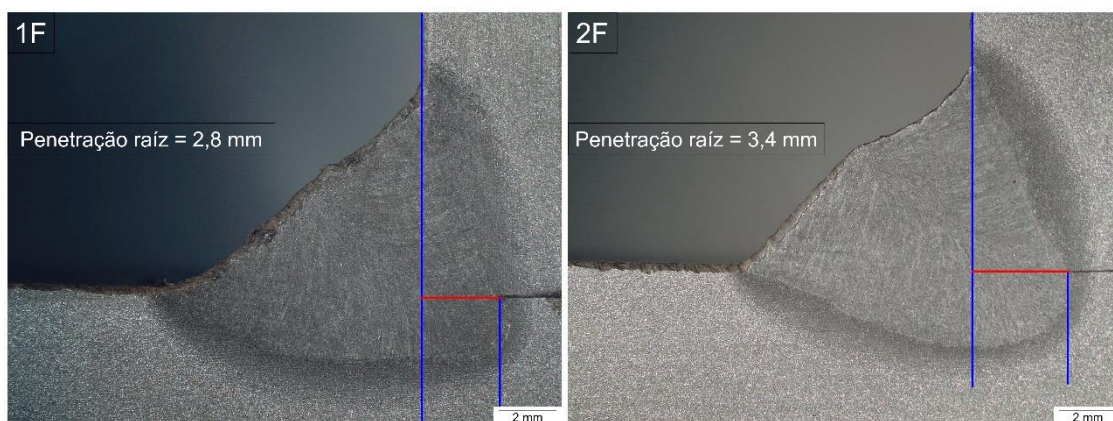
Dimensional mostrando a penetração de raiz associada aos testes in loco para cordão a5 nas posições 1F e 2F soldados após redefinição dos parâmetros de solda conforme Tabela 11.
